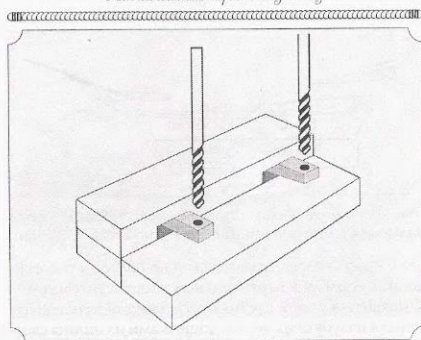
С одной стороны вставляют дополнительный штырек, соединяют части вместе и, перевернув, размечают отверстия под основные штыри
